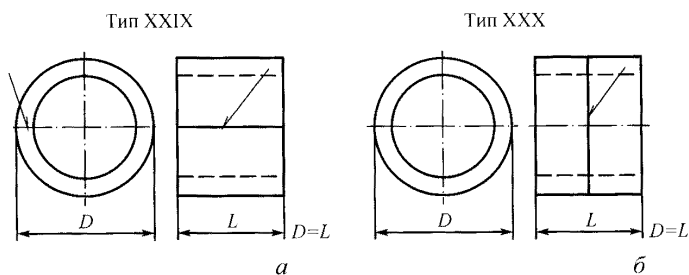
Сварные соединения. Образцы типов XXIX и XXX для испытания на изгиб труб с поперечным (а) и продольным (б) расположением швов: D – наружный диаметр трубы, мм; L – длина образца, мм
